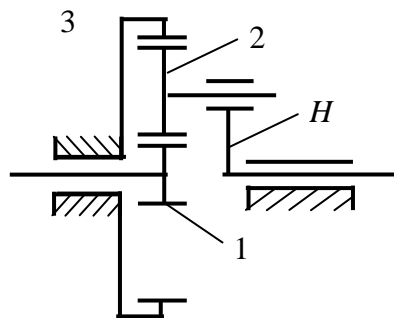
Схема планетарного зубчатого механизма (редуктор Джемса)
